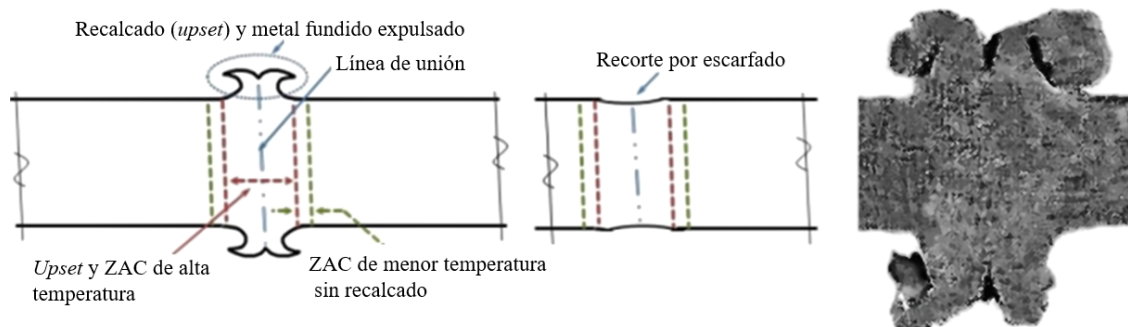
Conformación de los bordes longitudinales durante la soldadura ERW.
